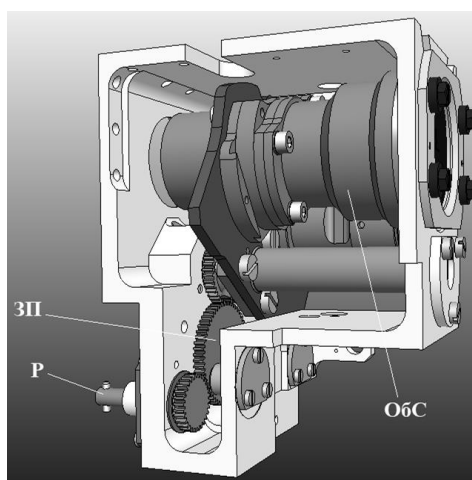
Внешний вид узла изменения увеличения в дневном канале: ЗП – зубчатая передача; Р – рукоятка переключения узкого-широкого полей зрения дневного канала; ОбС – оборачивающая система
